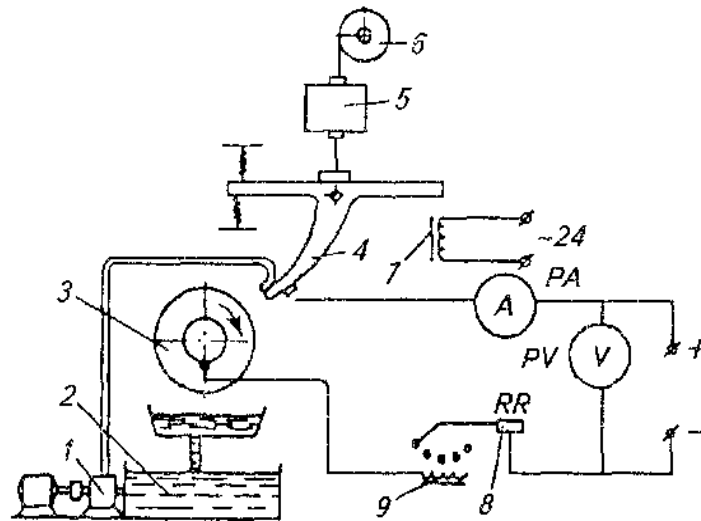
Схема установки для вібродугового наплавлення: 1 – насос; 2 – бак; 3 – деталь; 4 – мундштук; 5 – механізм для подачі; 6 – касета; 7 – вібратор; 9 – дросель; 8 – реостат [1, 2, 3, 6, 8, 9].
